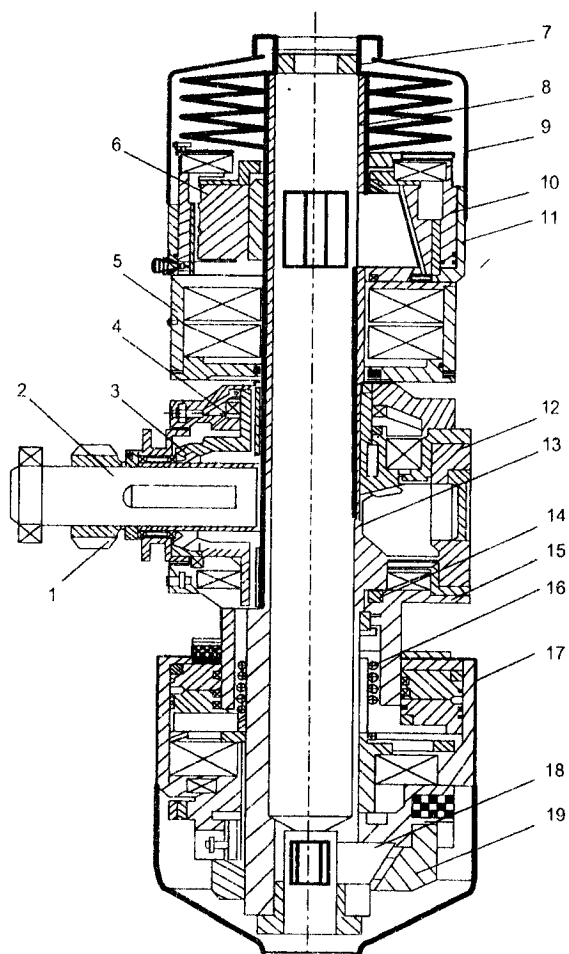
Обертач верстата СКБ-5: 1 – шестірня; 2 – вал; 3, 4 – конічні шестірни; 5 – траверса; 6, 19 – обойми; 7 – гайка; 8 – шпindelь; 9 – кожух; 10 – поршень; 11 – гідроциліндри патронів; 12 – корпус; 13 – привідна муфта; 14 – гайка; 15 – стакан; 16 – пружина; 18 – кулачки
